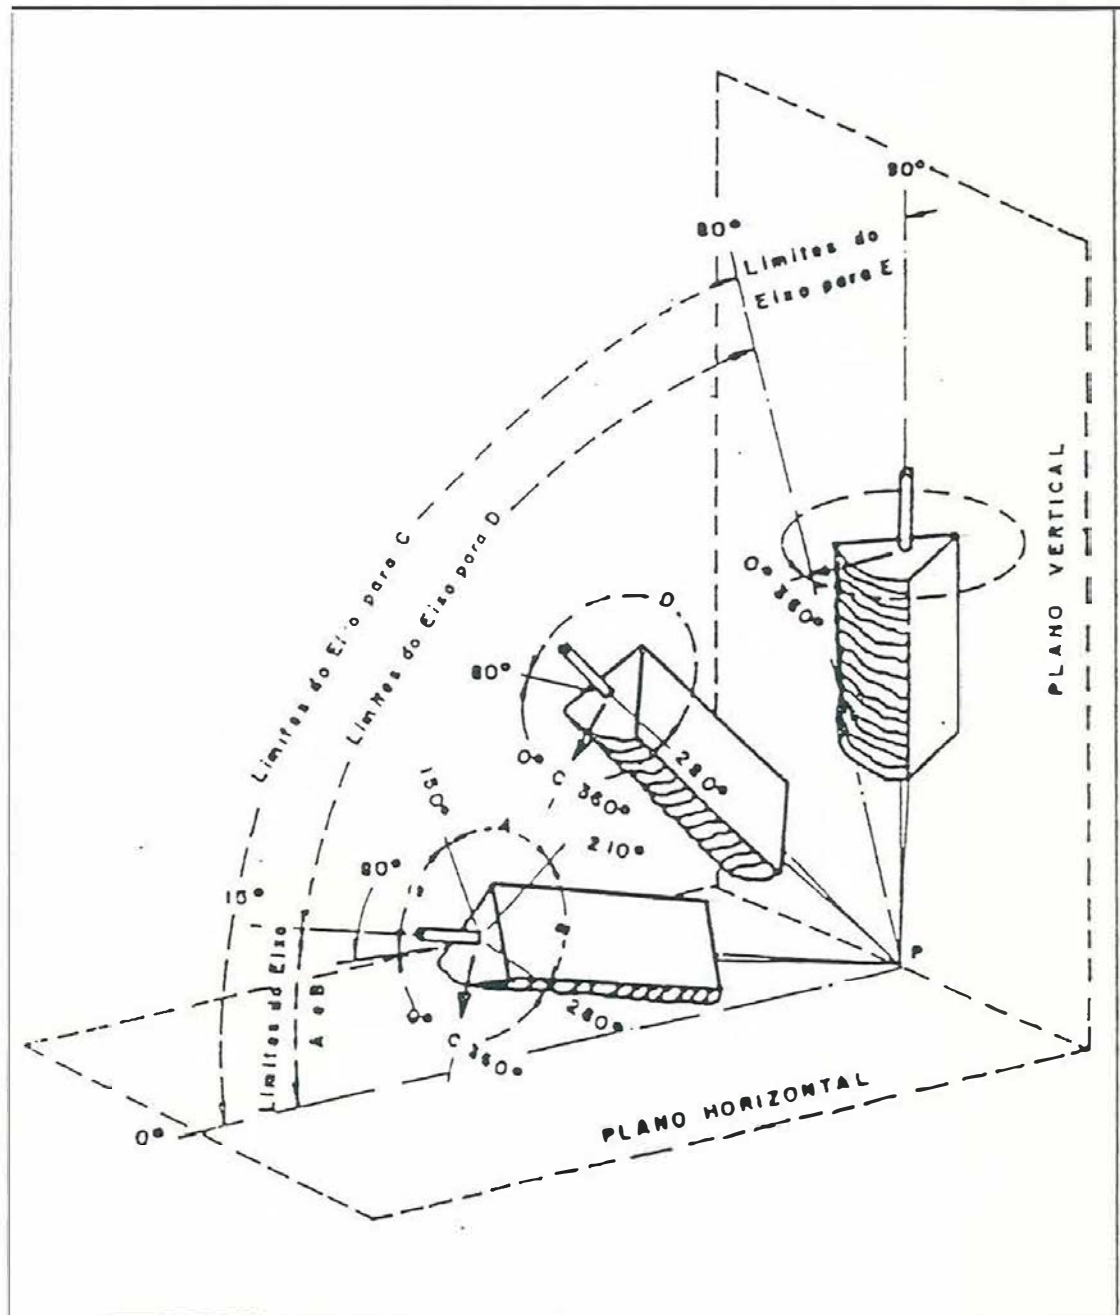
Tabulación de las posiciones de soldadura en junta biseada.
